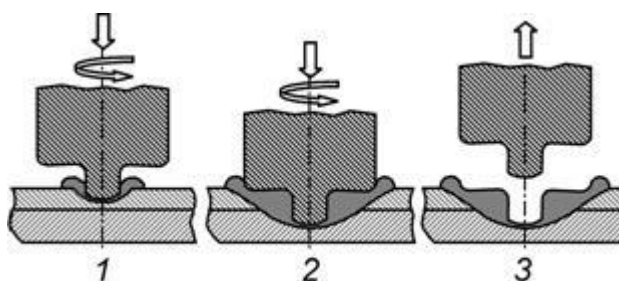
Стадии формирования сварного соединения при точечной сварке трением.
